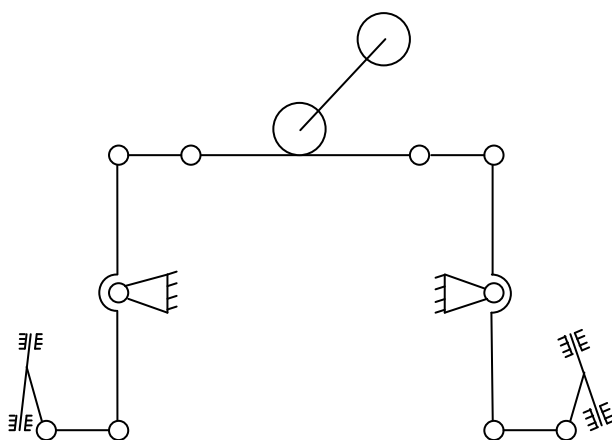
Кинематическая схема рулевого управления типа шестерня-рейка с маятниковыми рычагами
